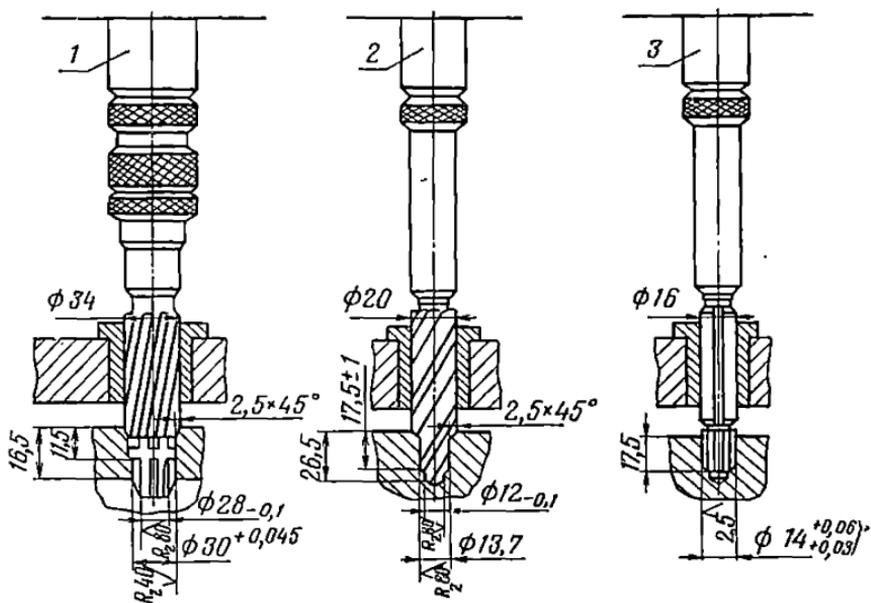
Обработка отверстий головки цилиндров двигателя СМД-14 комбинированным инструментом:
